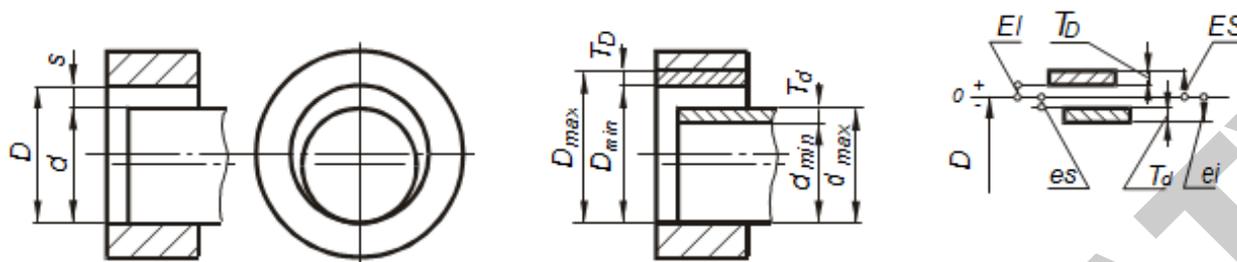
Посадка с зазором и схема расположения полей допусков
